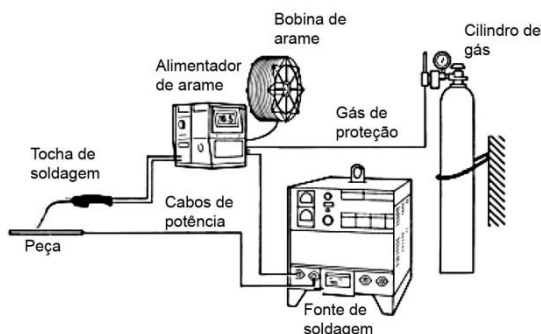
Componentes do processo de soldagem MIG/MAG (Gohr (2002) [28], adaptado).
